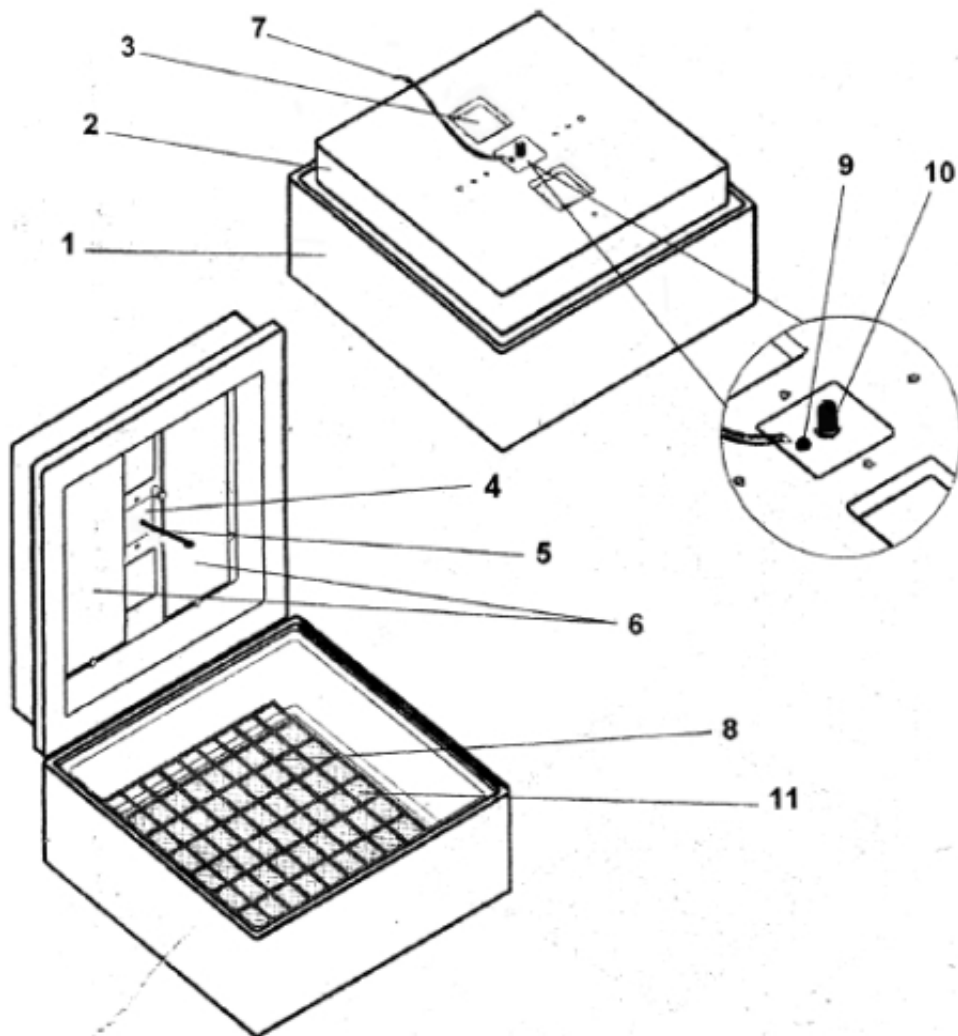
Устройство бытового инкубатора; «Несушка»
